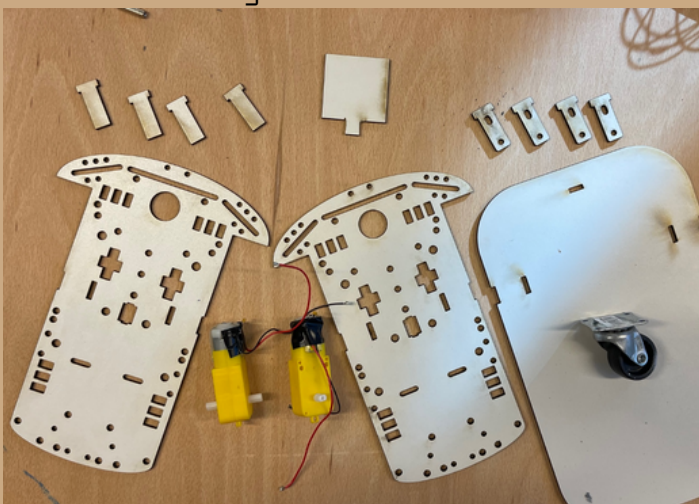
ensemble des pièces réalisées à la découpeuse laser
